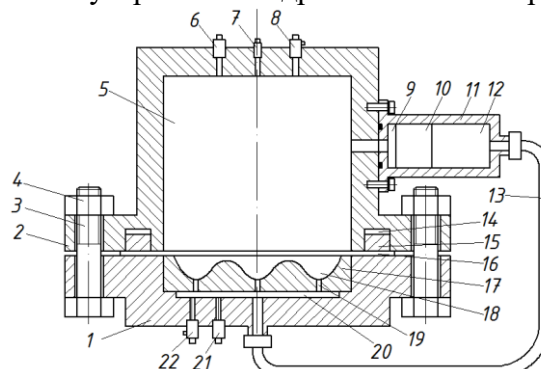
Схема устройства для листовой газовой формовки с противодавлением
